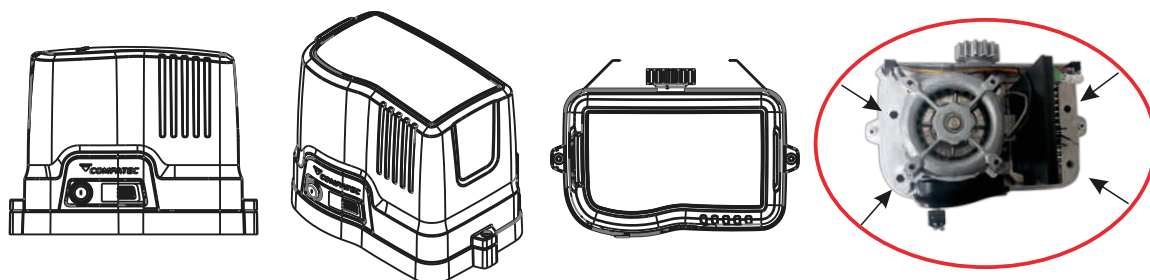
Para fixar as base do Kit ao corpo do Movimentador Deslizante e necessário remover a tampa.
